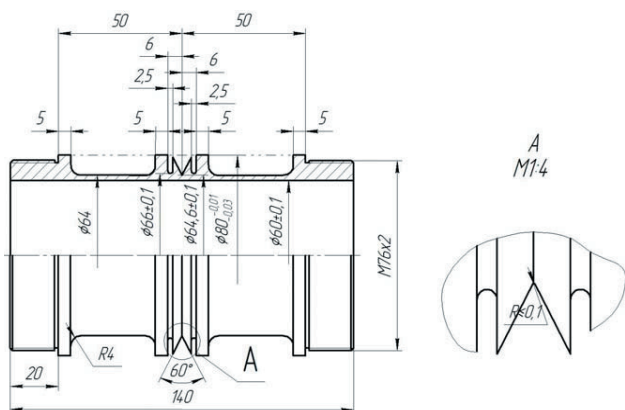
Конструкція зразка індикатора різбового з'єднання 3-121 для випробування на опір втомі
